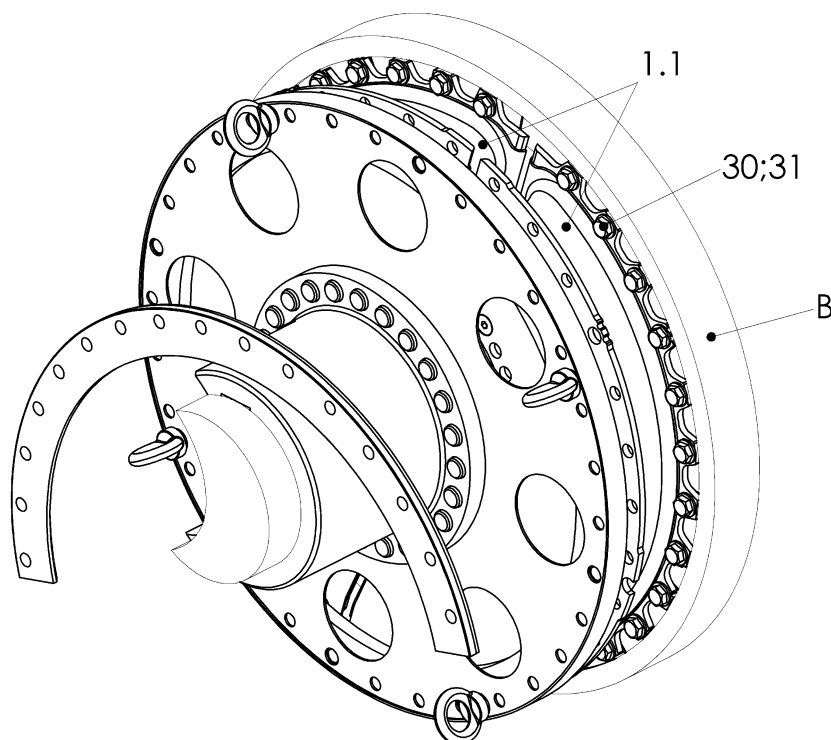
Gummielemente am Schwungrad verschrauben
